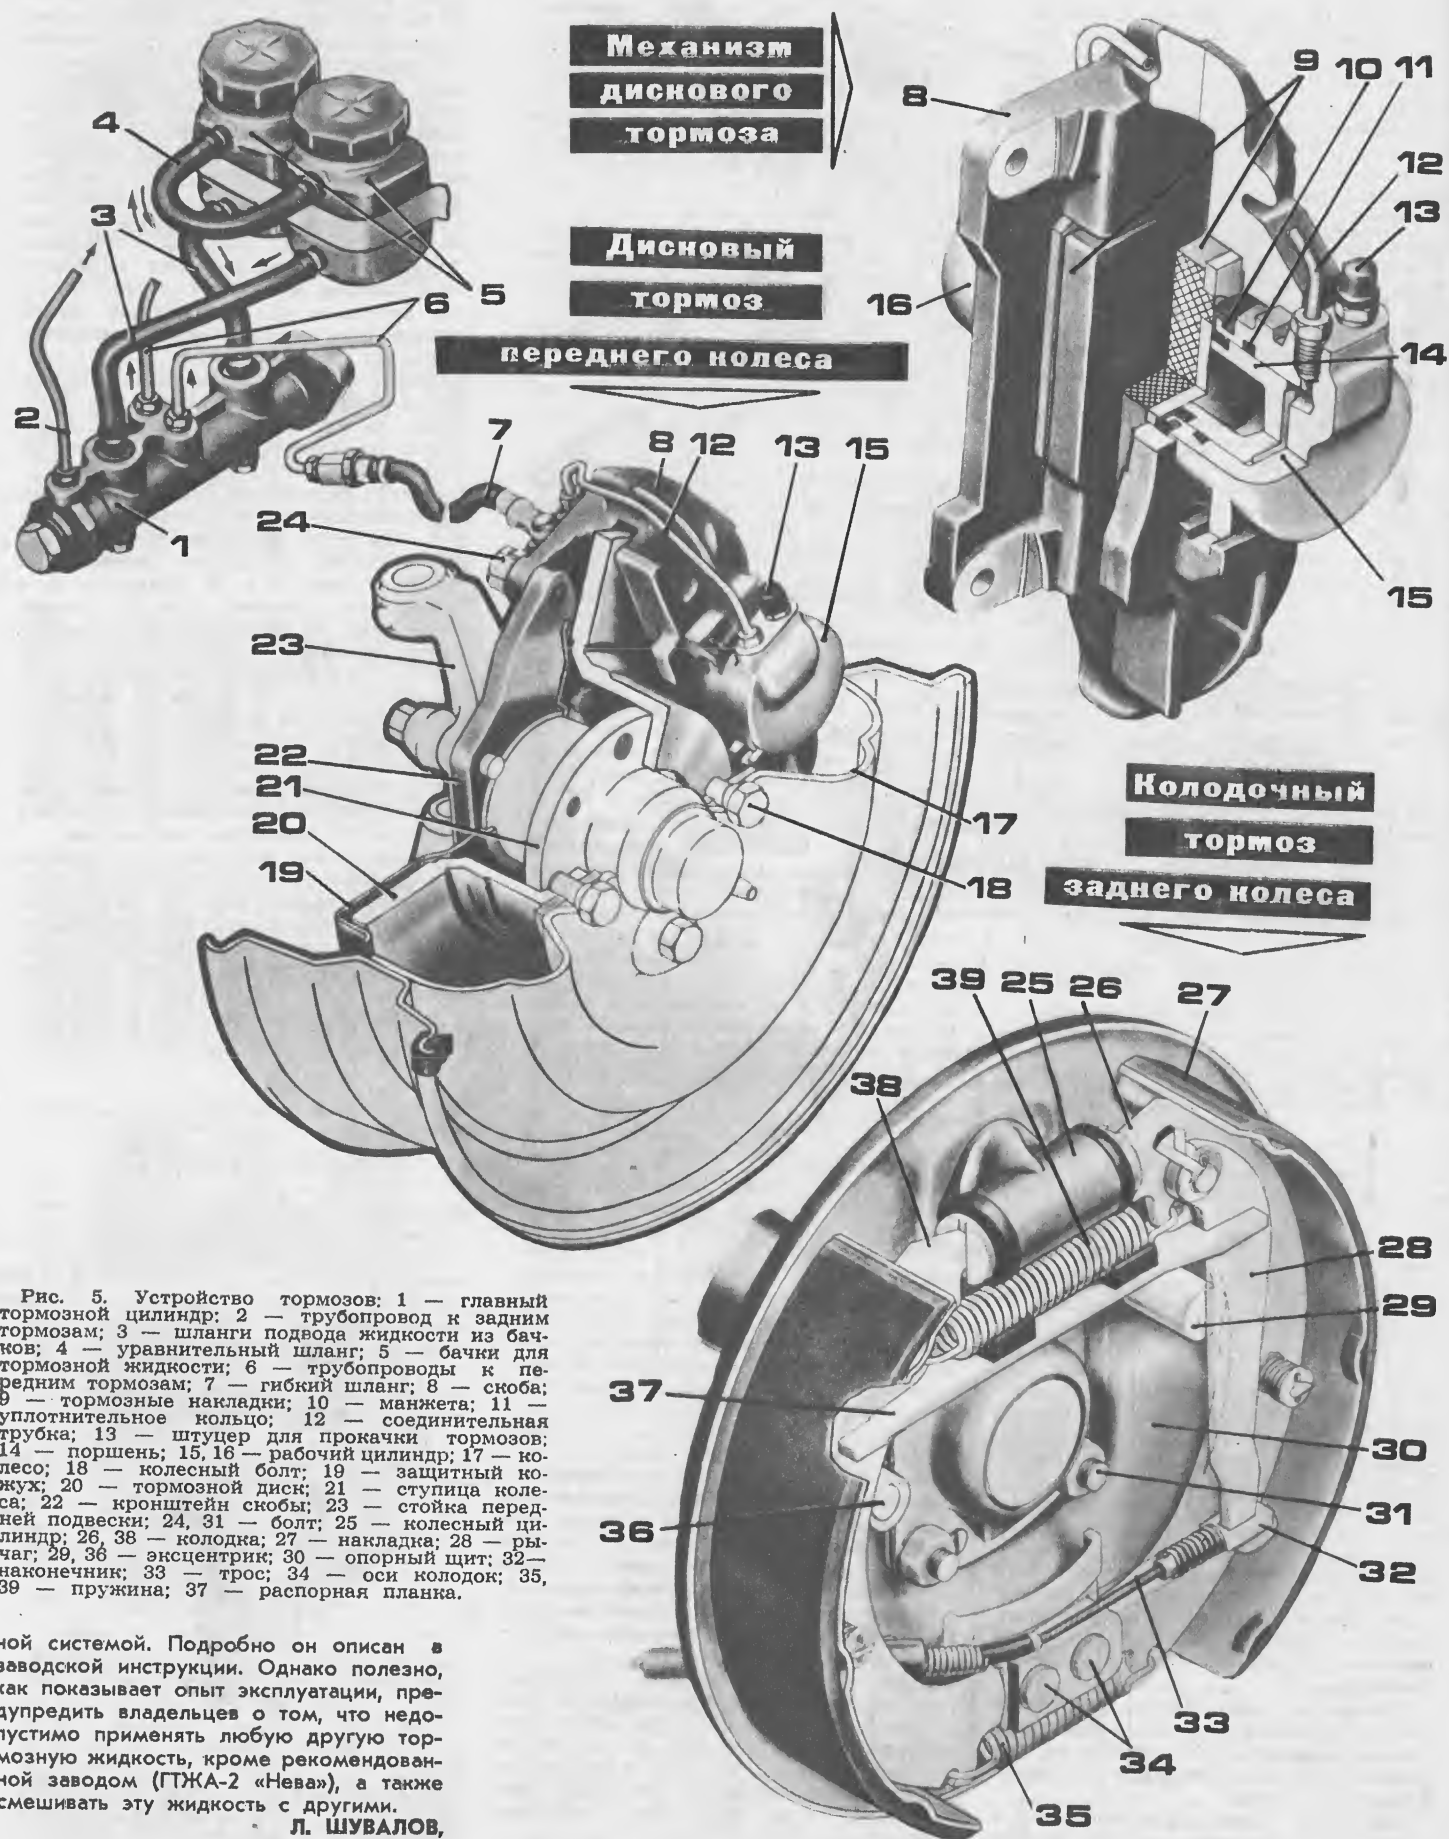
Устройство тормозов: 1 — главный тормозной цилиндр; 2 — трубопровод к задним тормозам; 3 — шланги подвода жидкости из баков; 4 — уравнительный шланг; 5 — бачки для тормозной жидкости; 6 — трубопроводы к передним тормозам; 7 — гибкий шланг; 8 — скоба; 9 — тормозные накладки; 10 — манжета; 11 — уплотнительное кольцо; 12 — соединительная трубка; 13 — штуцер для прокачки тормозов; 14 — поршень; 15, 16 — рабочий цилиндр; 17 — колесо; 18 — колесный болт; 19 — защитный кожух; 20 — тормозной диск; 21 — ступица колеса; 22 — кронштейн скобы; 23 — стойка передней подвески; 24, 31 — болт; 25 — колесный цилиндр; 26, 38 — колодка; 27 — накладка; 28 — рычаг; 29, 36 — эксцентрик; 30 — опорный щит; 32 — наконечник; 33 — трос; 34 — оси колодок; 35, 39 — пружина; 37 — распорная планка.
